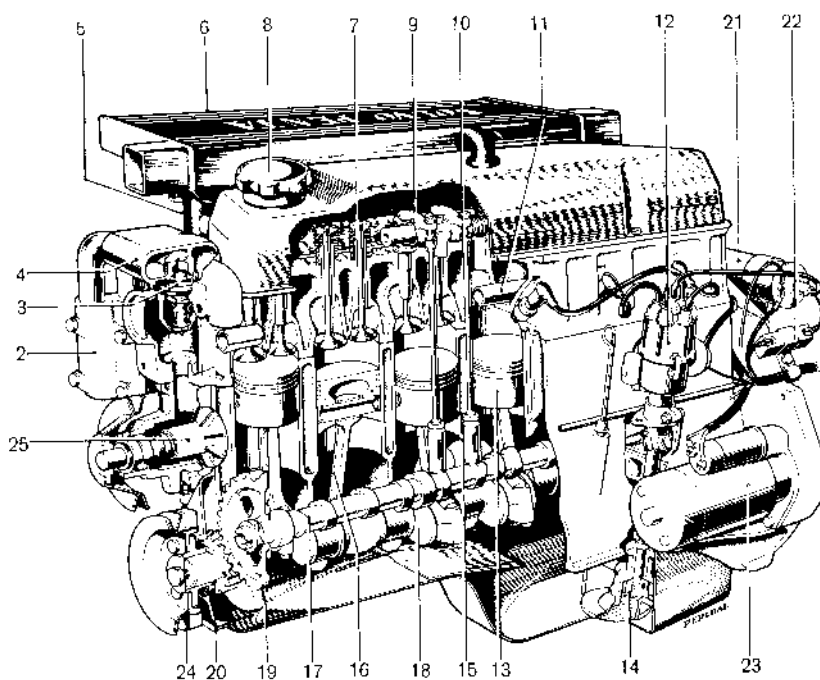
Genomskäring av 6-cylindrig motor, typ AQ170
